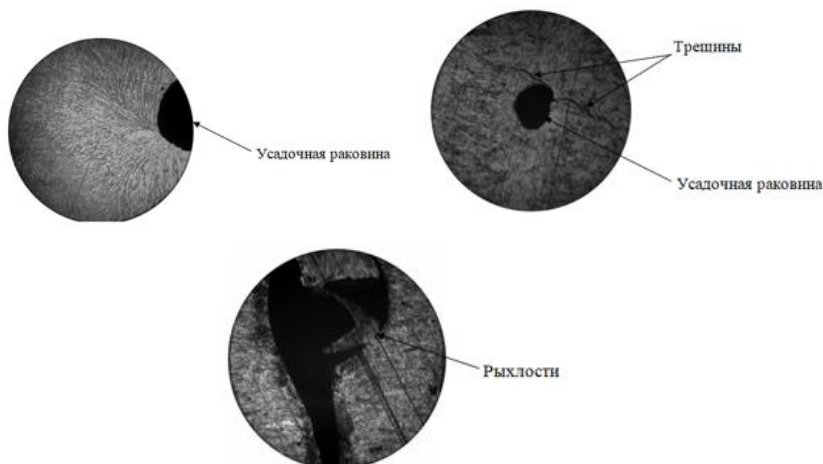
Дефекты литой зоны сварного соединения
